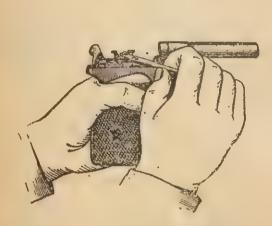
Снятие крючка пружины шептала с затворной задержки
